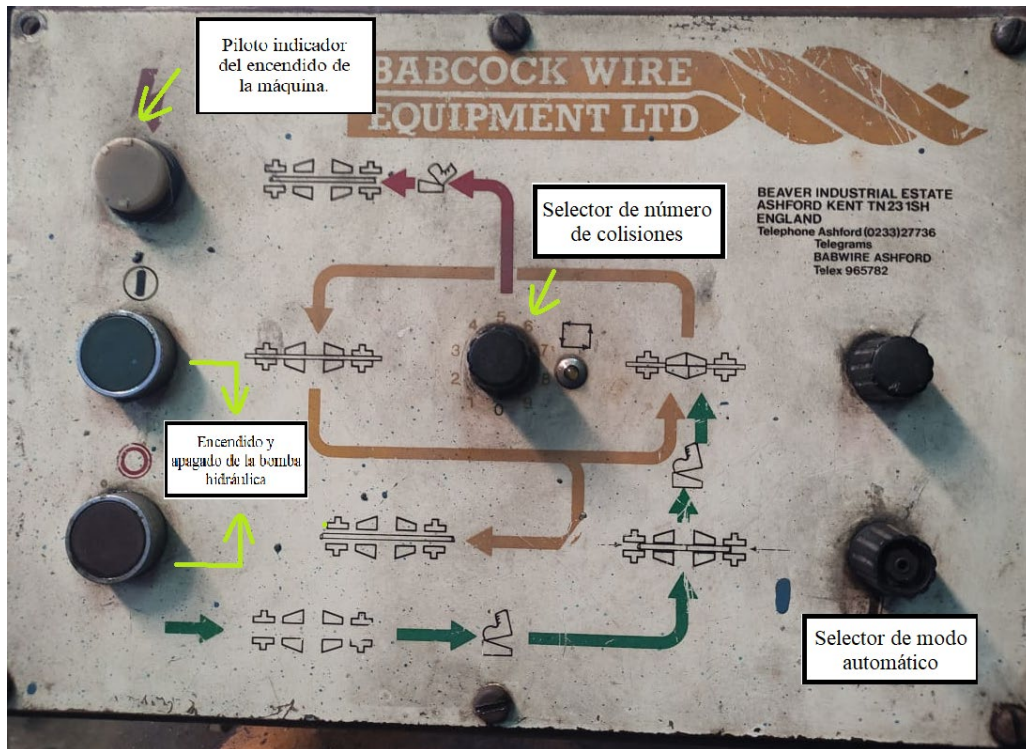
Panel de Control de la máquina Soldadora.
